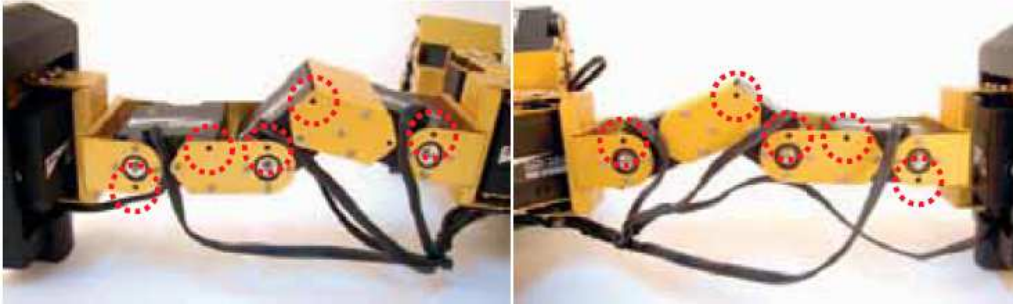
Instalación de los cables sujetadores en ambas piernas
